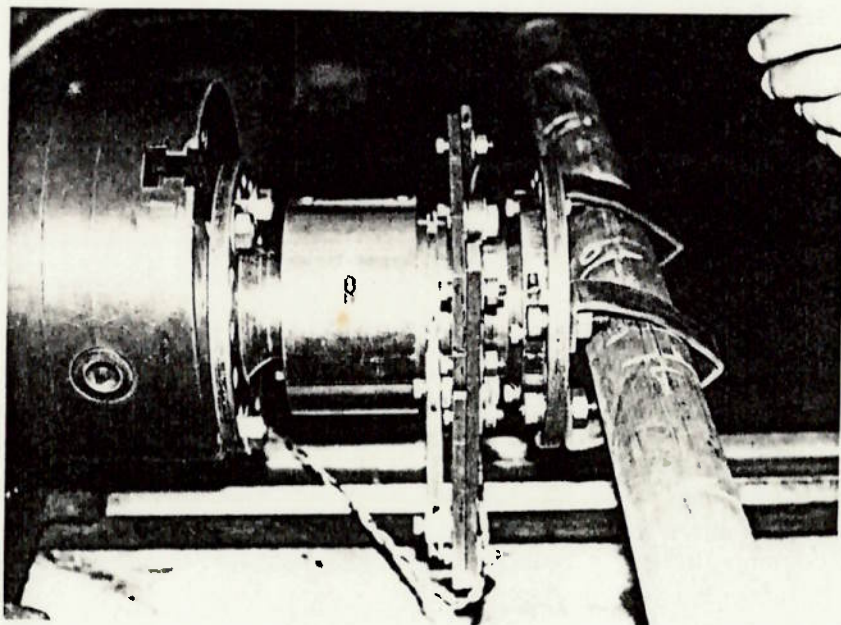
TD0/FM montado para calibração estática: vemos o TD0/FM fixo por uma das flanges à placa travada de um torno mecânico; e a barra cilíndrica, usado como braço de alavanca para aplicação de torque, fixa à outra flange.
